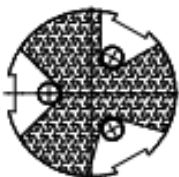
Фрезер забойный типа ФЗ среднего вида
